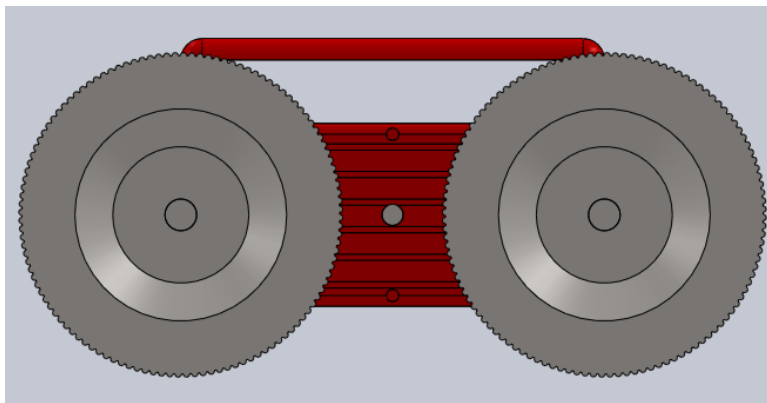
Ensamble de las ruedas con el sistema de engranajes
